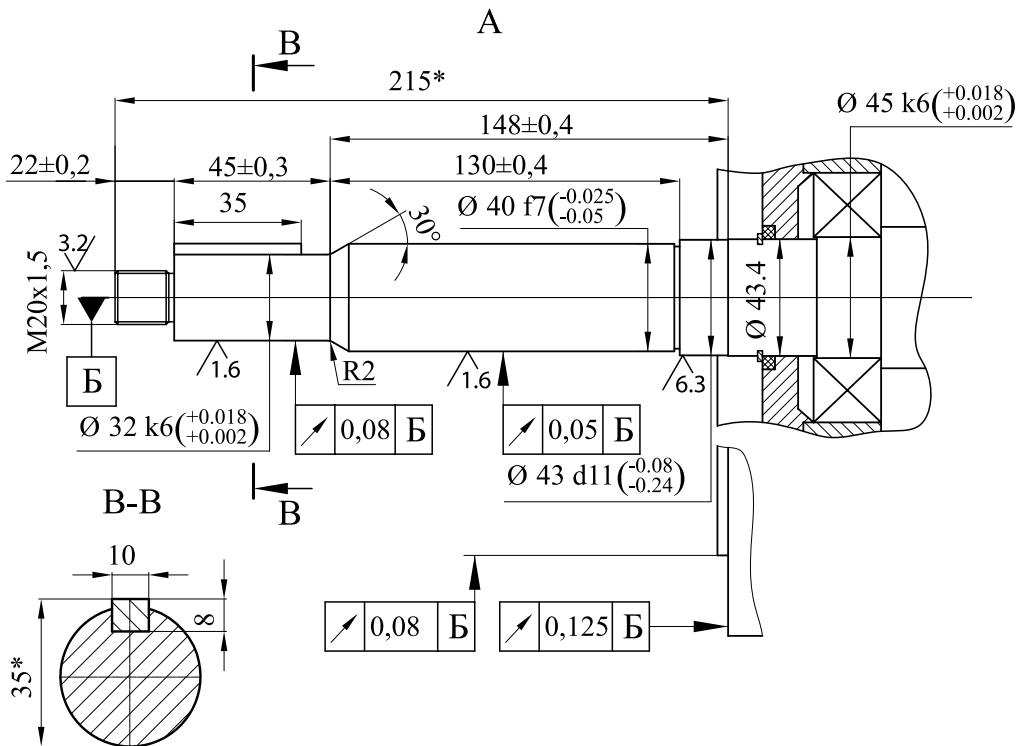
Свободный конец вала двигателя 6АМУ160S2ЖУ2
